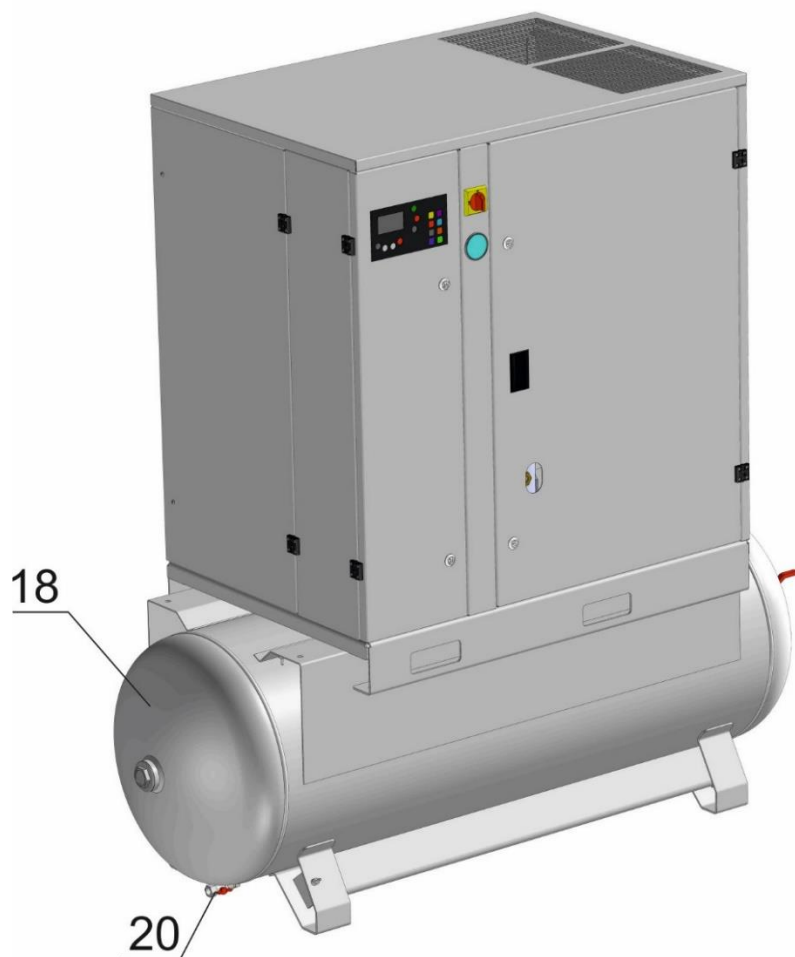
Общий вид компрессорных установок ВК25-...-500(BC), ВК30-...-500(BC)
